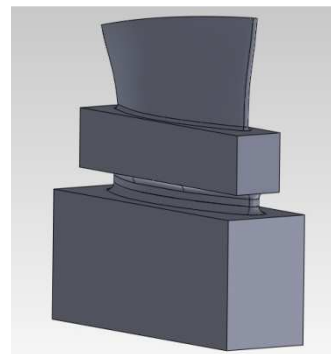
Заготовка образца, имитирующего сварное соединение диска и лопатки в блиске
